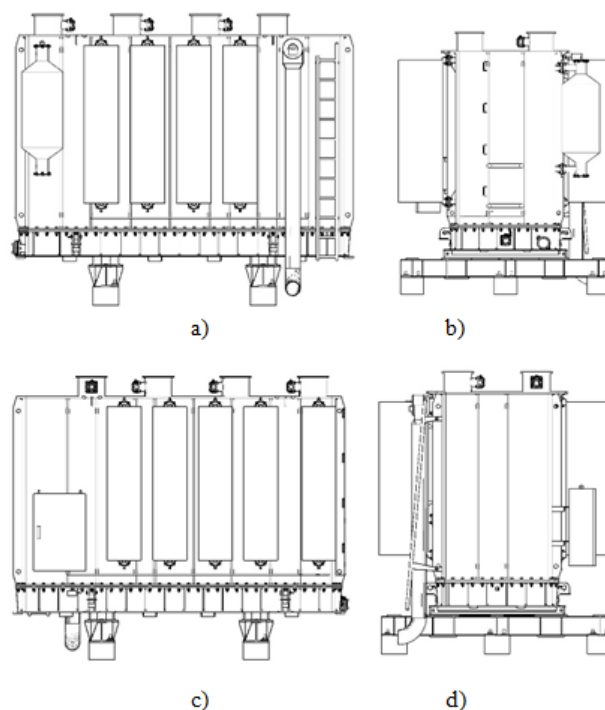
Чертеж бака понижающего трансформатора, выполненный на основе скан-файла: а) вид спереди; б) вид слева; в) вид сзади; д) вид справа
